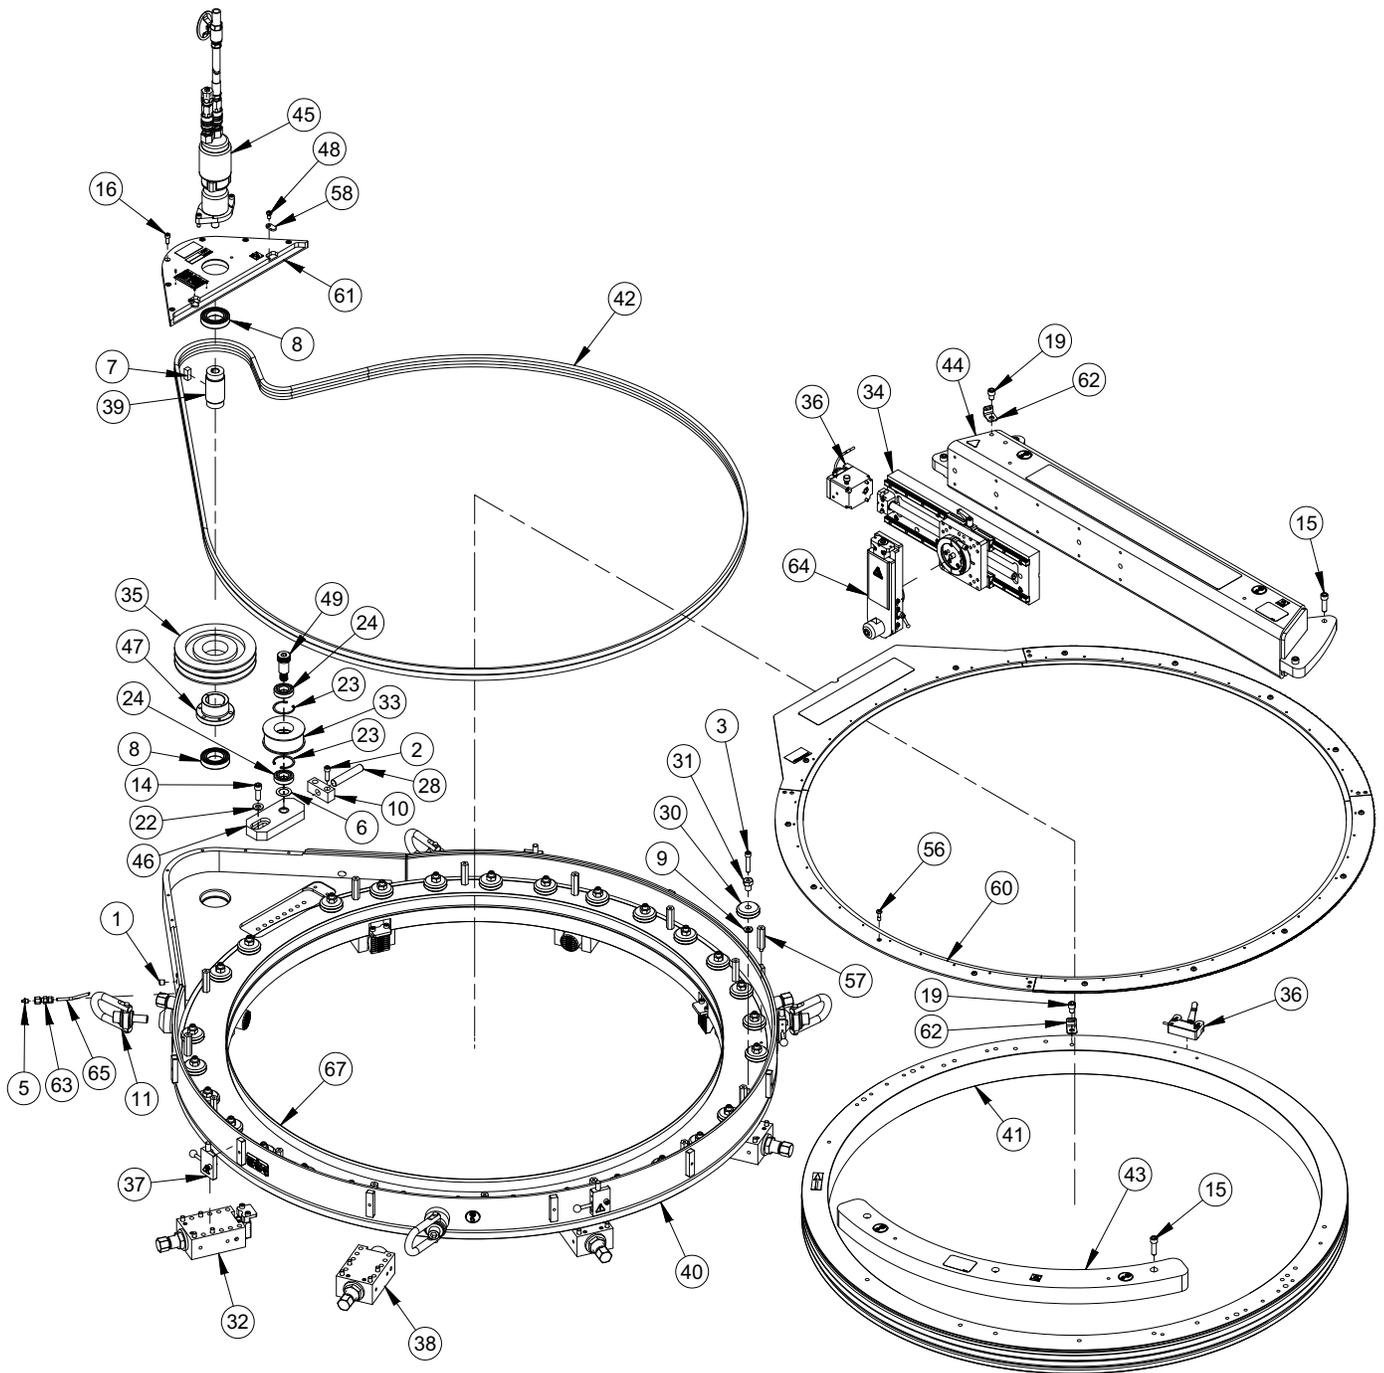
ODF50 SPEED FACER ENSEMBLE (RÉF. 86980)
